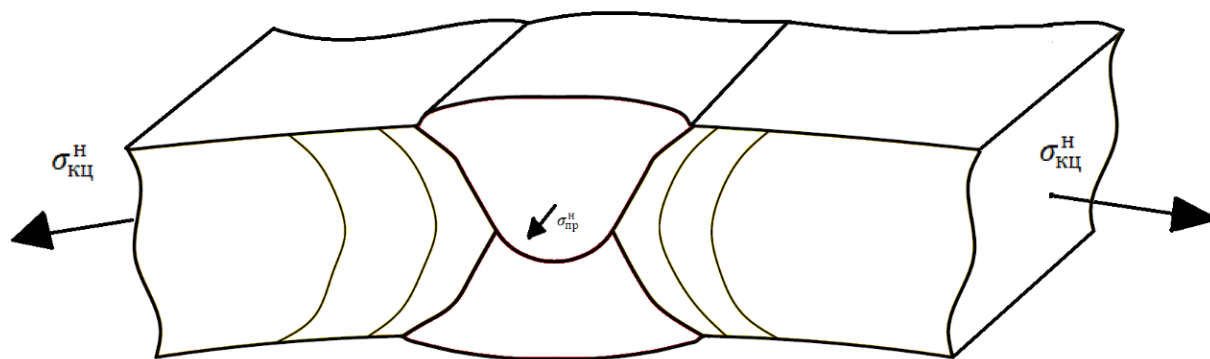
Схема нагружения продольного сварного соединения
